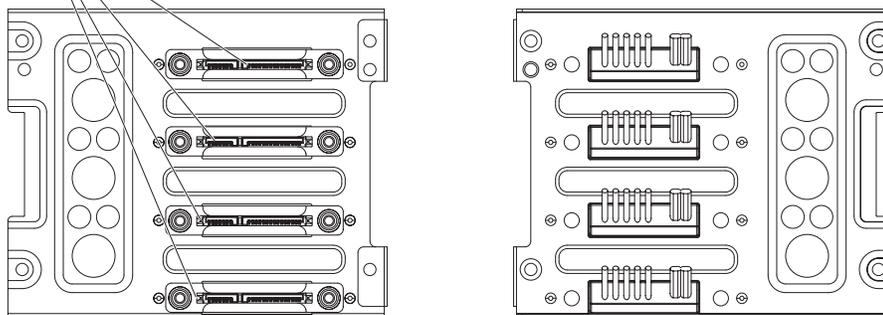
Connecteurs de l'assemblage de plaque arrière d'unités de disque dur 3,5 pouces
